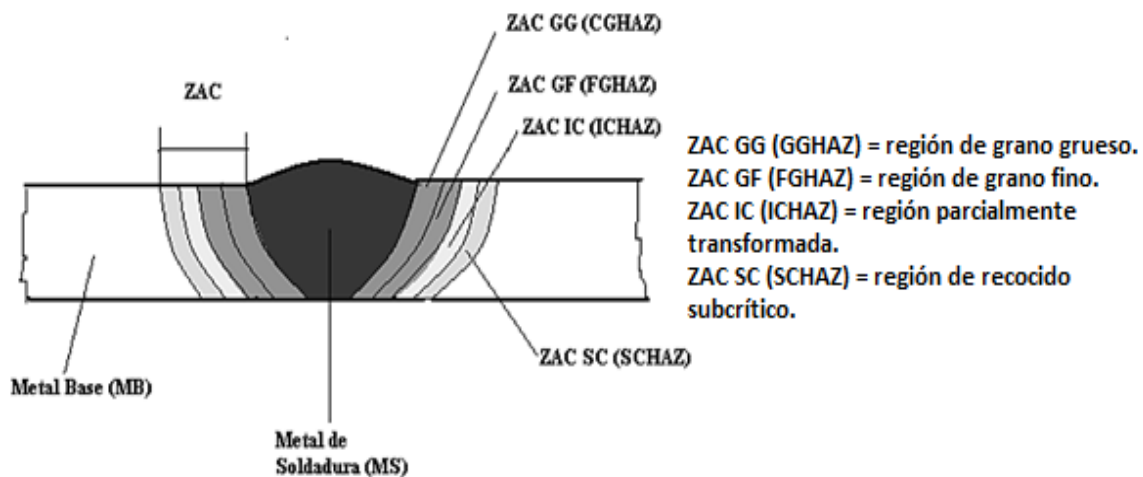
Zonas afectadas en el proceso de soldadura SMAW [11].
